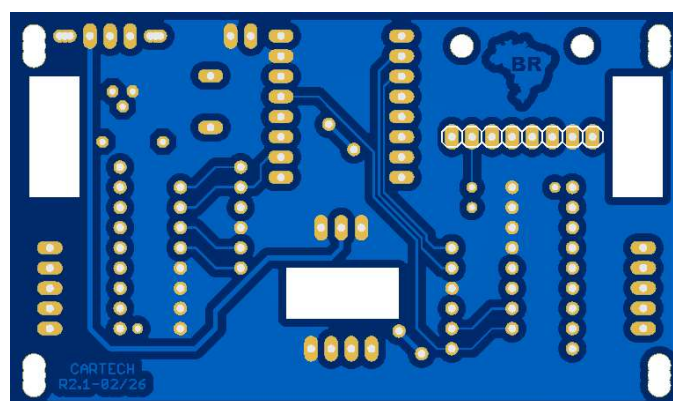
Placa CARTECH rev. 2.1 (lado da solda)
